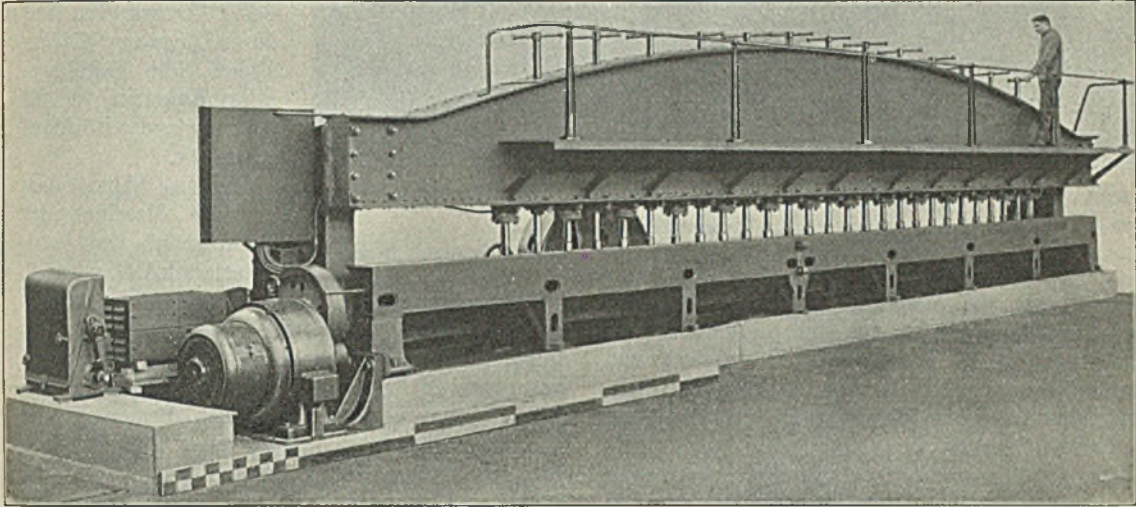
Blechkanten-Hobelmaschine von E. Schieß A. G., Düsseldorf.
